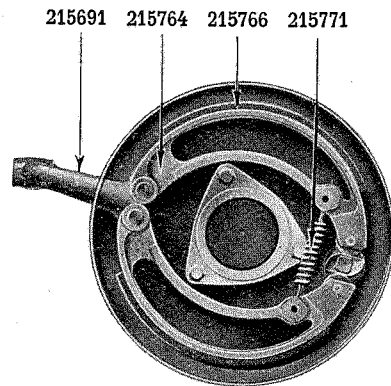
L'essieu arrière. Vue des segments de frein.
